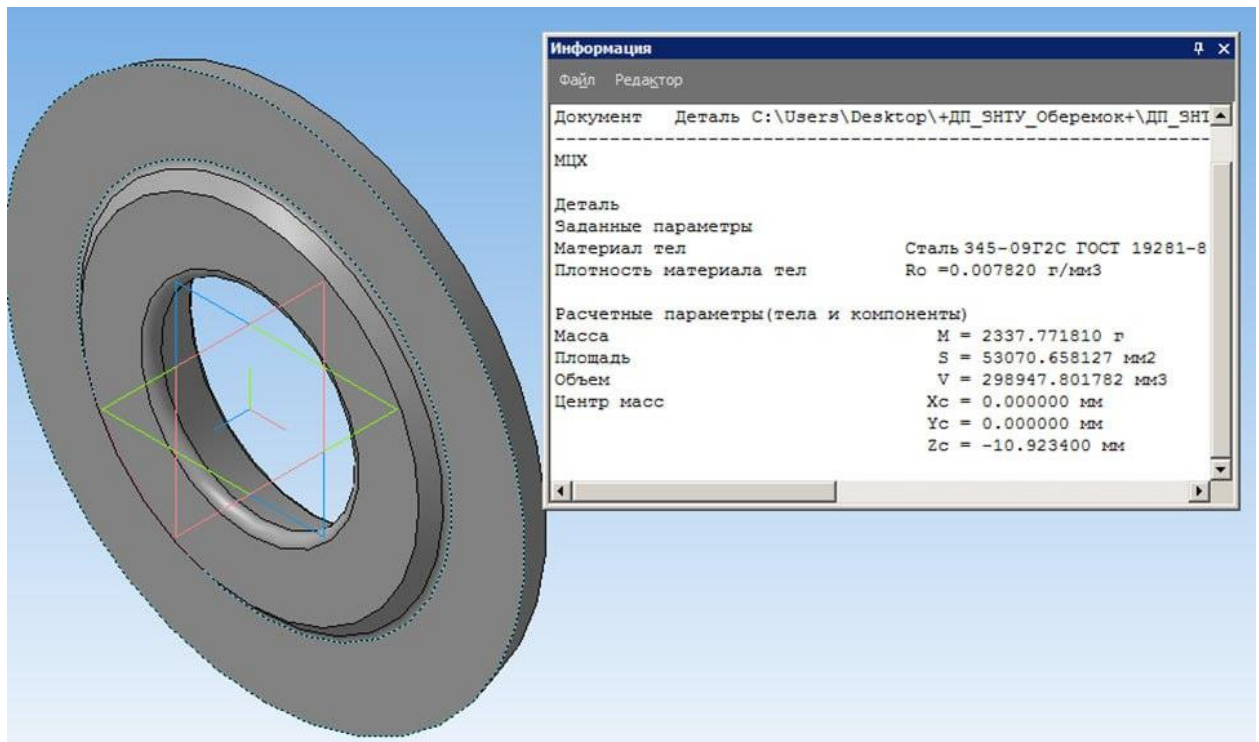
Тривимірна модель заготовки штамповка на ГКМ
